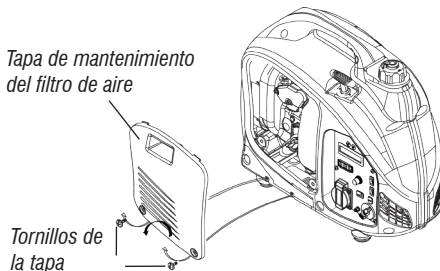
Removiendo la tapa de mantenimiento del filtro de aire
